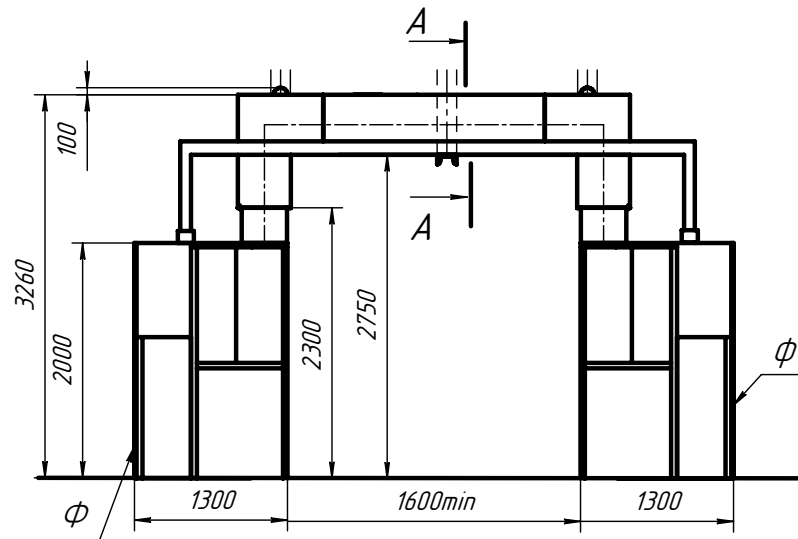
Габаритные, установочные, присоединительные размеры шкафов.
